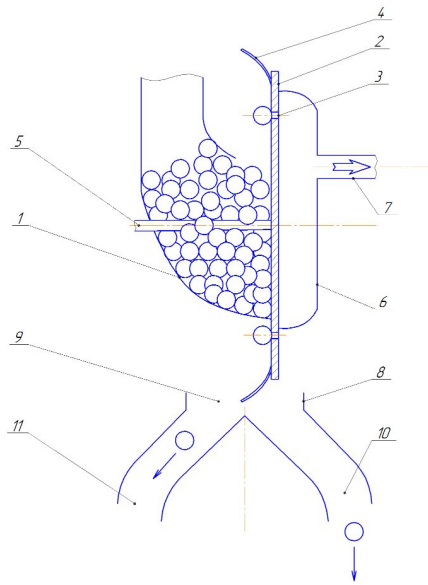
Пневматичний апарат для дворядкового висіву: 1 – камера заповнення; 2 – висівний диск; 3 – отвори комірок диска; 4 – пластинчастий направляч; 5 – приводний вал диска; 6 – вакуумна камера; 7 – патрубок; 8 – вхідний відвід; 9 – вхідний канал; 10 і 11 – вихідні канали.
